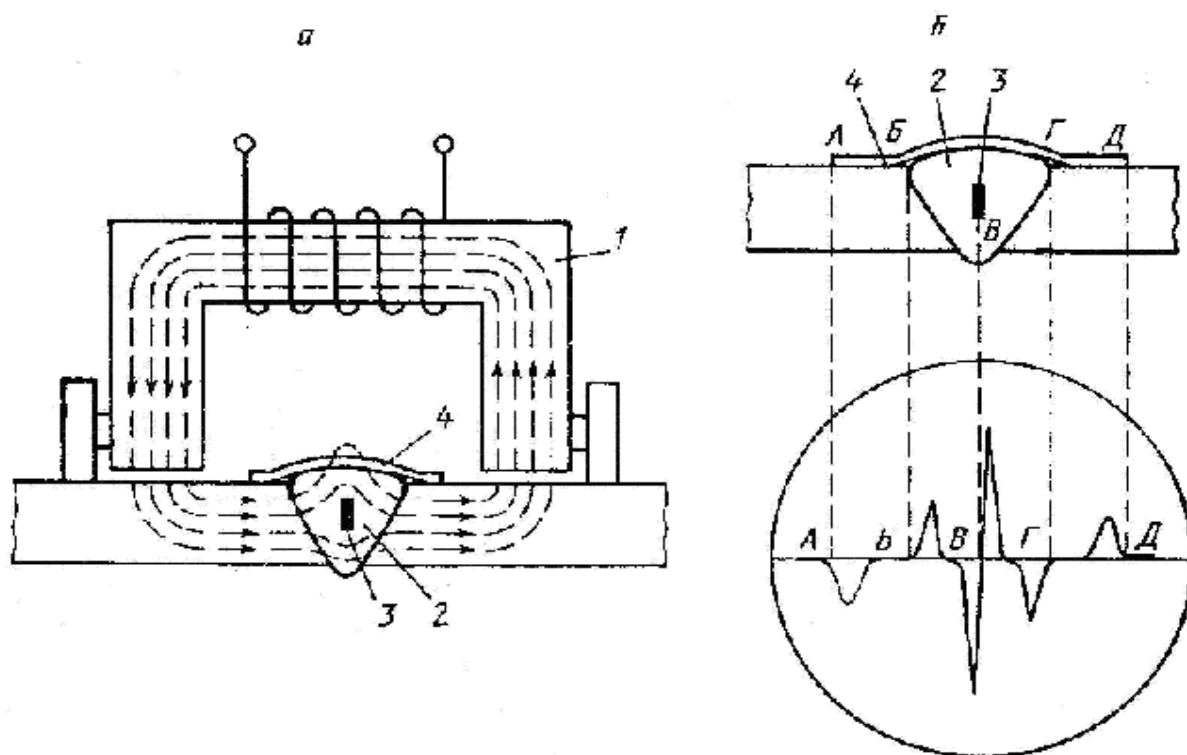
Схема магнитографического контроля сварного шва:
